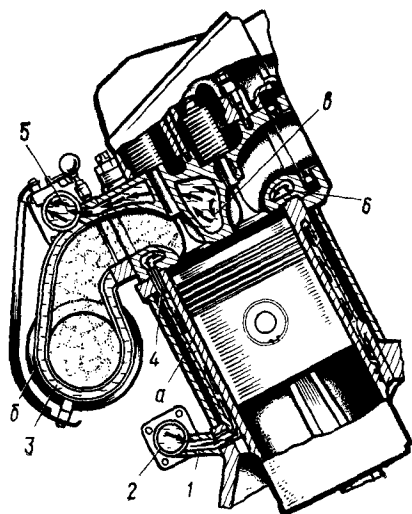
Схема охлаждения цилиндра и крышки дизеля 2А-5Д49:
